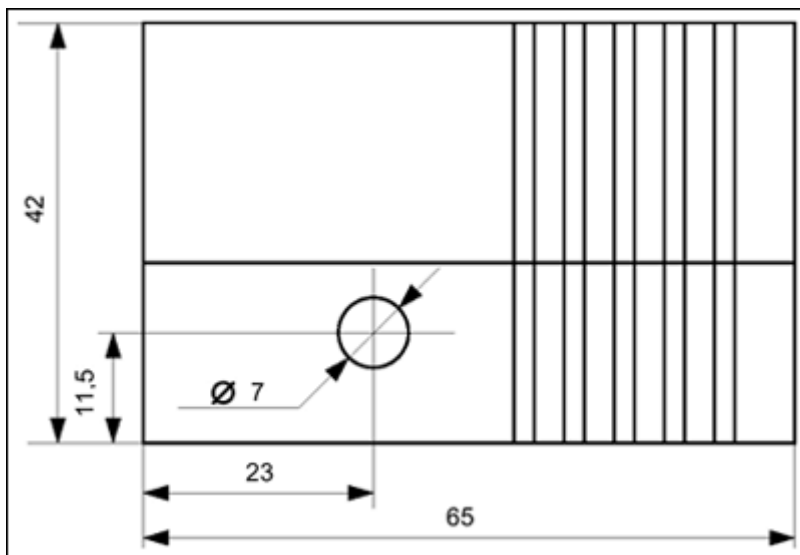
Отверстие на боковой поверхности корпуса под телефонный разъем.
